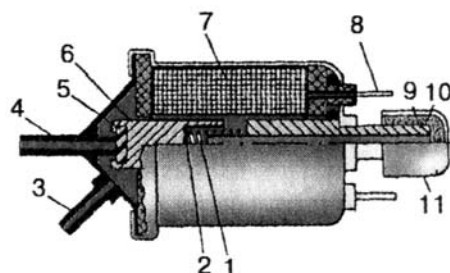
Электромагнитный клапан: 1 - пружина; 2 и 5 - клапаны; 3 - штуцер соединения с карбюратором; 4 - штуцер соединения со впускной трубой; 6 – сердечник; 7 - обмотка; 8 - штекер; 9 - атмосферный штуцер; 10 - фильтр; 11 - защитный колпачок
